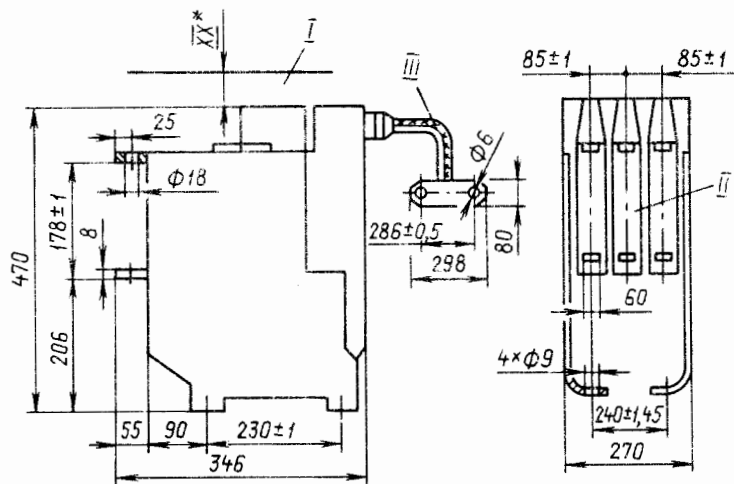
Габаритные и установочные размеры выключателей Э06С с электродвигательным приводом в двух- и трехполюсном исполнении:
